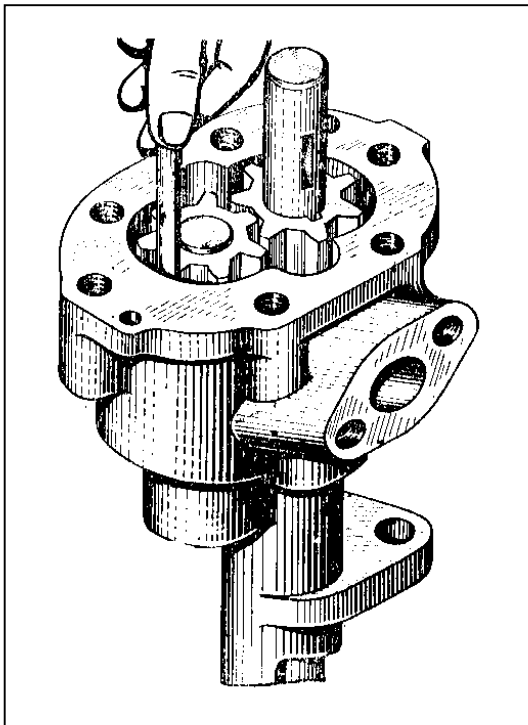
Контроль радиального зазора между вершинами зубьев колес и гнездами корпуса.
